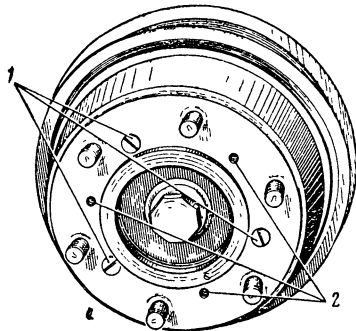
Тормозной барабан переднего колеса автомобиля ГАЗ-51:
